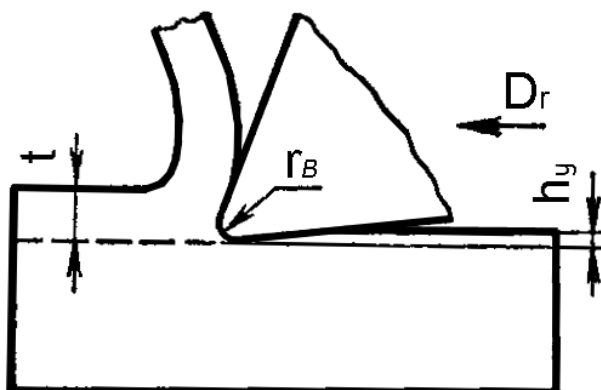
Схема образования поверхностного слоя заготовки
